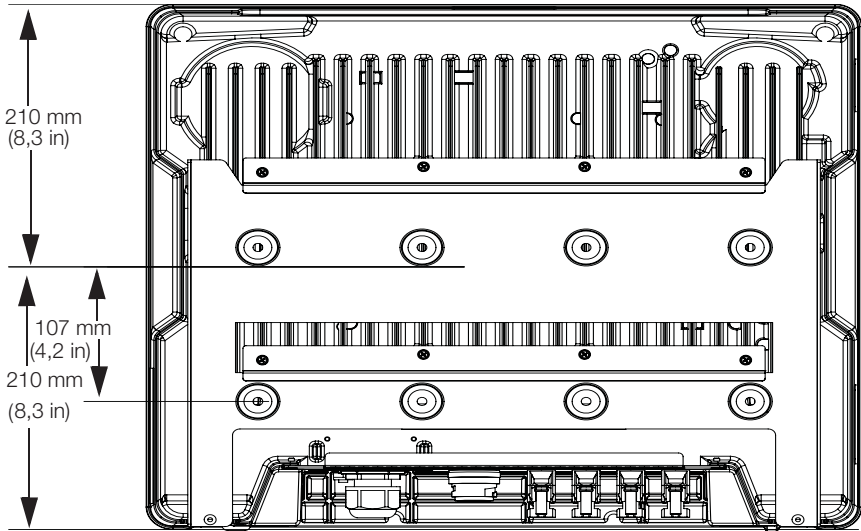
Posición de la placa de montaje (vista trasera del inversor)
